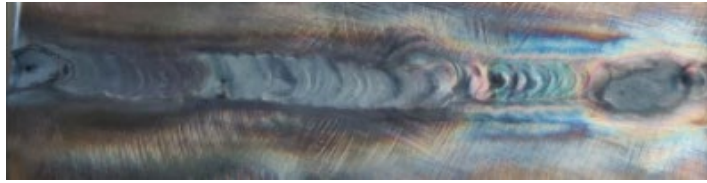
Soldadura TIG realizada pelo autor
